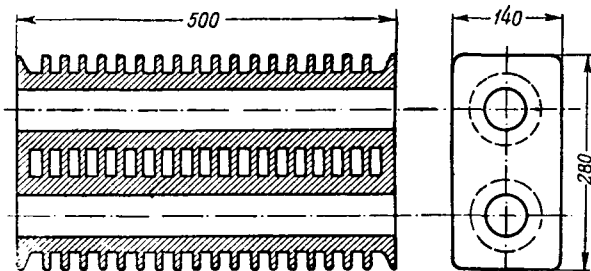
Корпус блока сопротивления из алюминиевой отливки.
